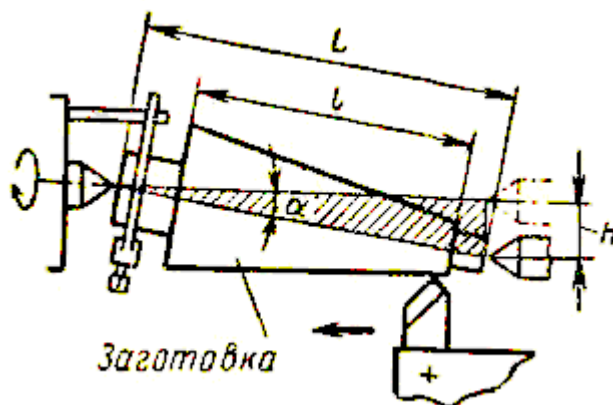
Обработка наружной конической поверхности способом смещения корпуса задней бабки
